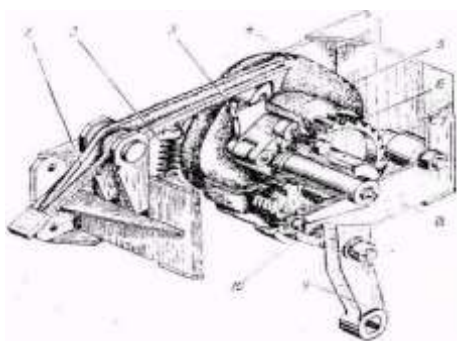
Механизм привода обматывающего шпагата: 1 - защелка; 2 - пружина; 3 - собачка; 4 — кулачок; 5 - ведущая часть муфты; 6 - храповик; 7, 10 - собачка; 8 - корпус; 9 - рычаг.
